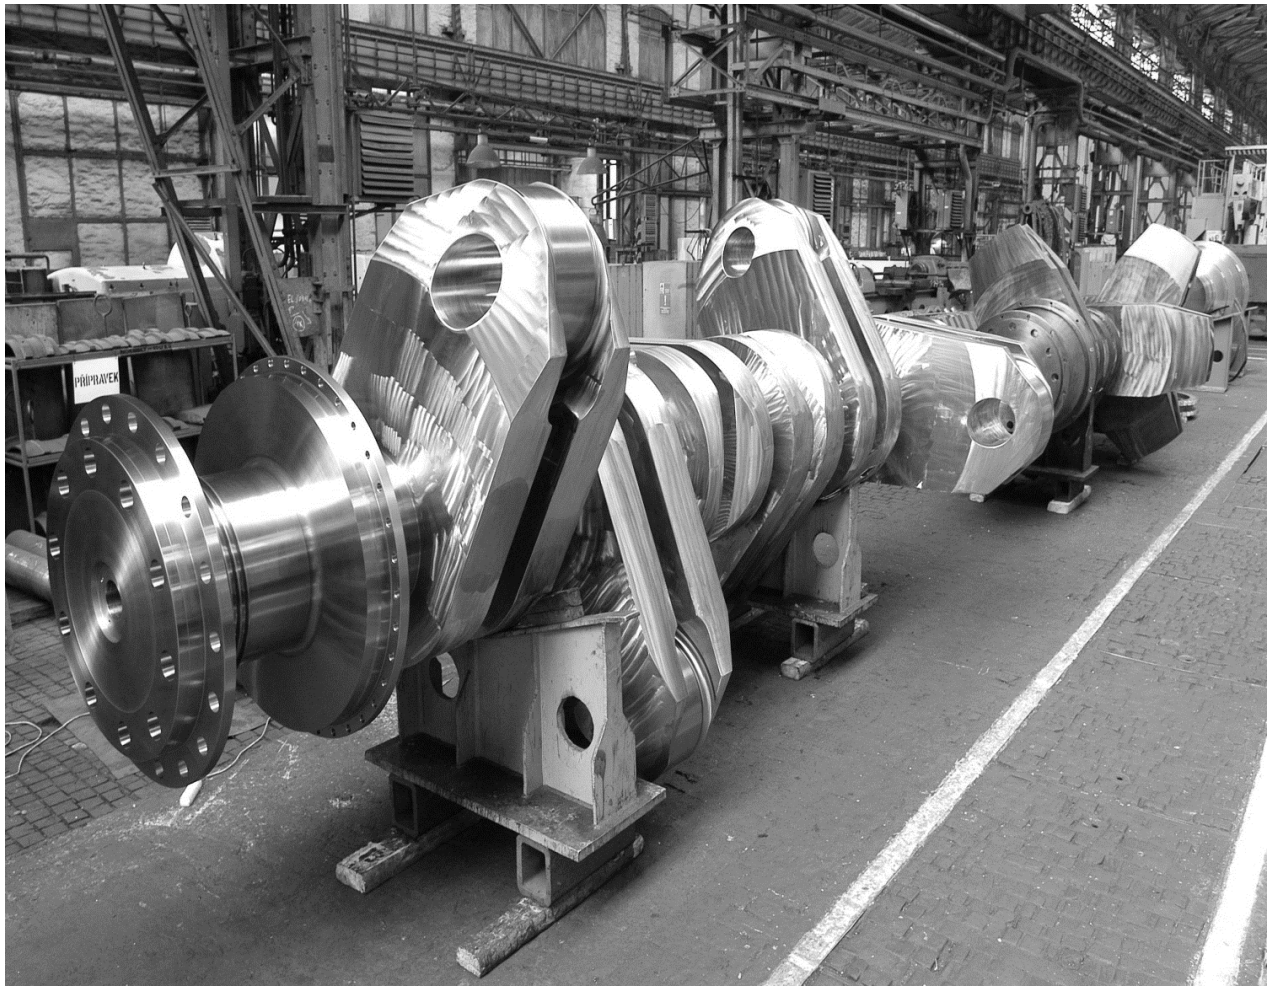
Колінчатий вал двигуна Mitsubishi 8AX33B
